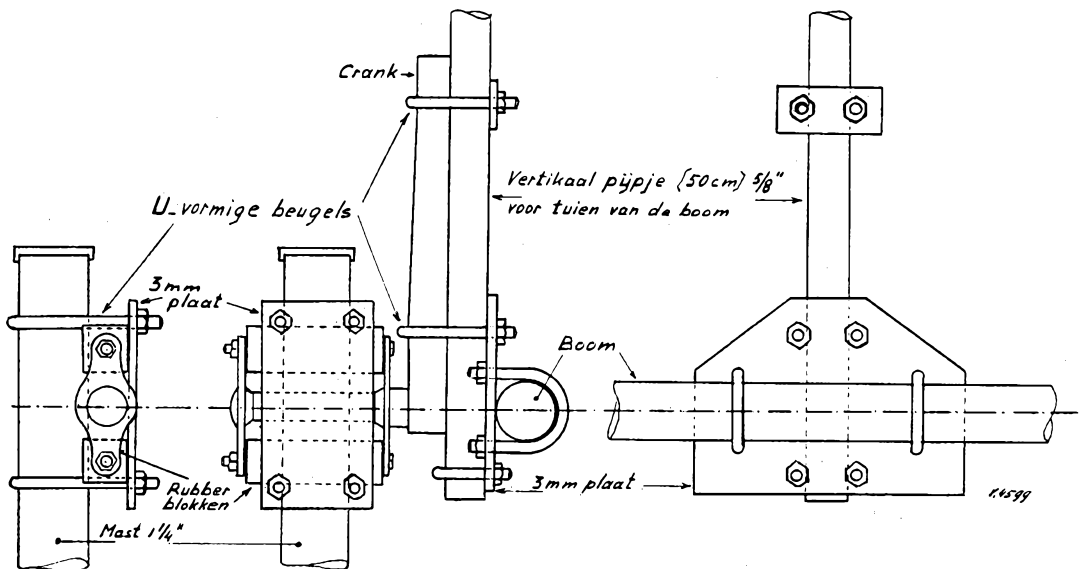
Constructie van het draaipunt. Hoofdbestanddeel: een fietstrapper met rubberblokjes en crank
